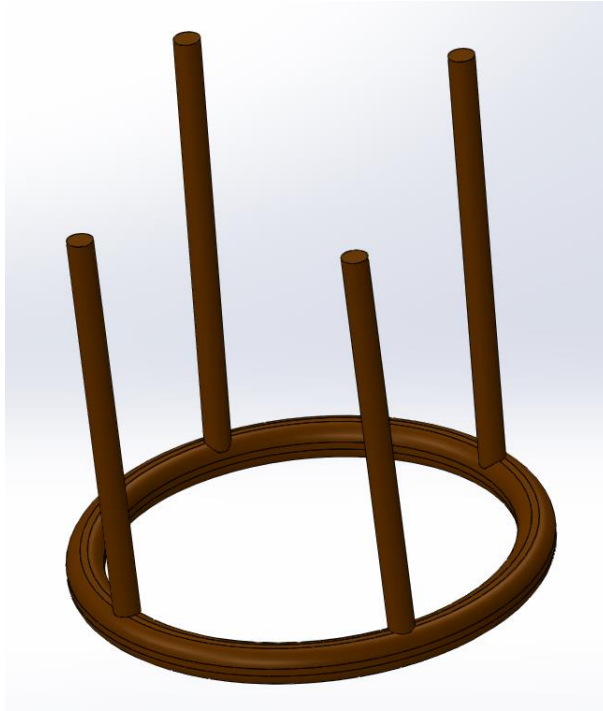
Cola o Parte inferior la cual ira soldada con la parte media y es con la que estará unida con la cadena y los grilletes.
